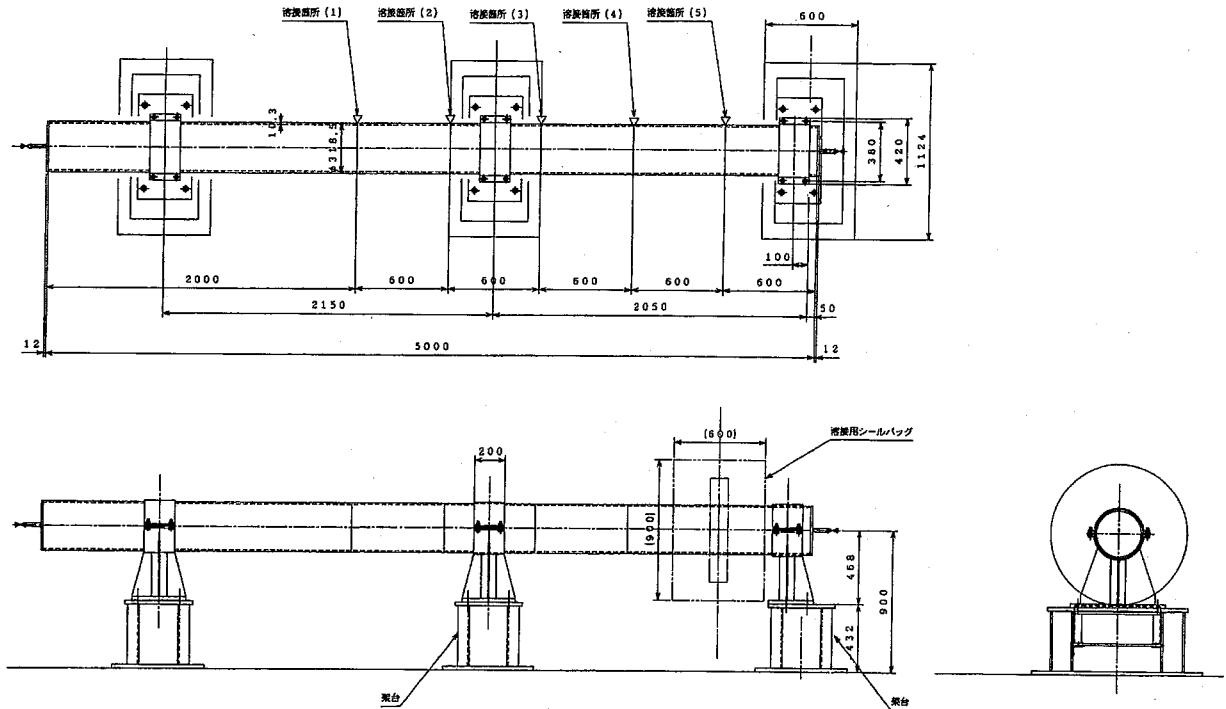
(4/4) 要素試験体の構造図 (2 次主冷却系配管 (STPA24))
